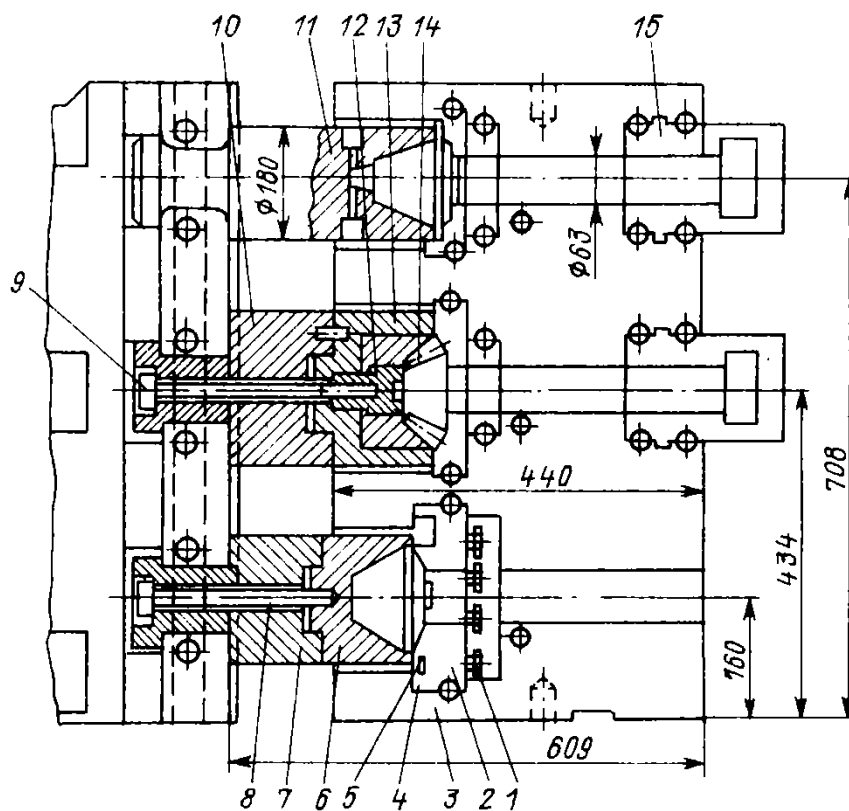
Штамп для точной штамповки конической шестерни со штампованным зубом и длинным хвостовиком
